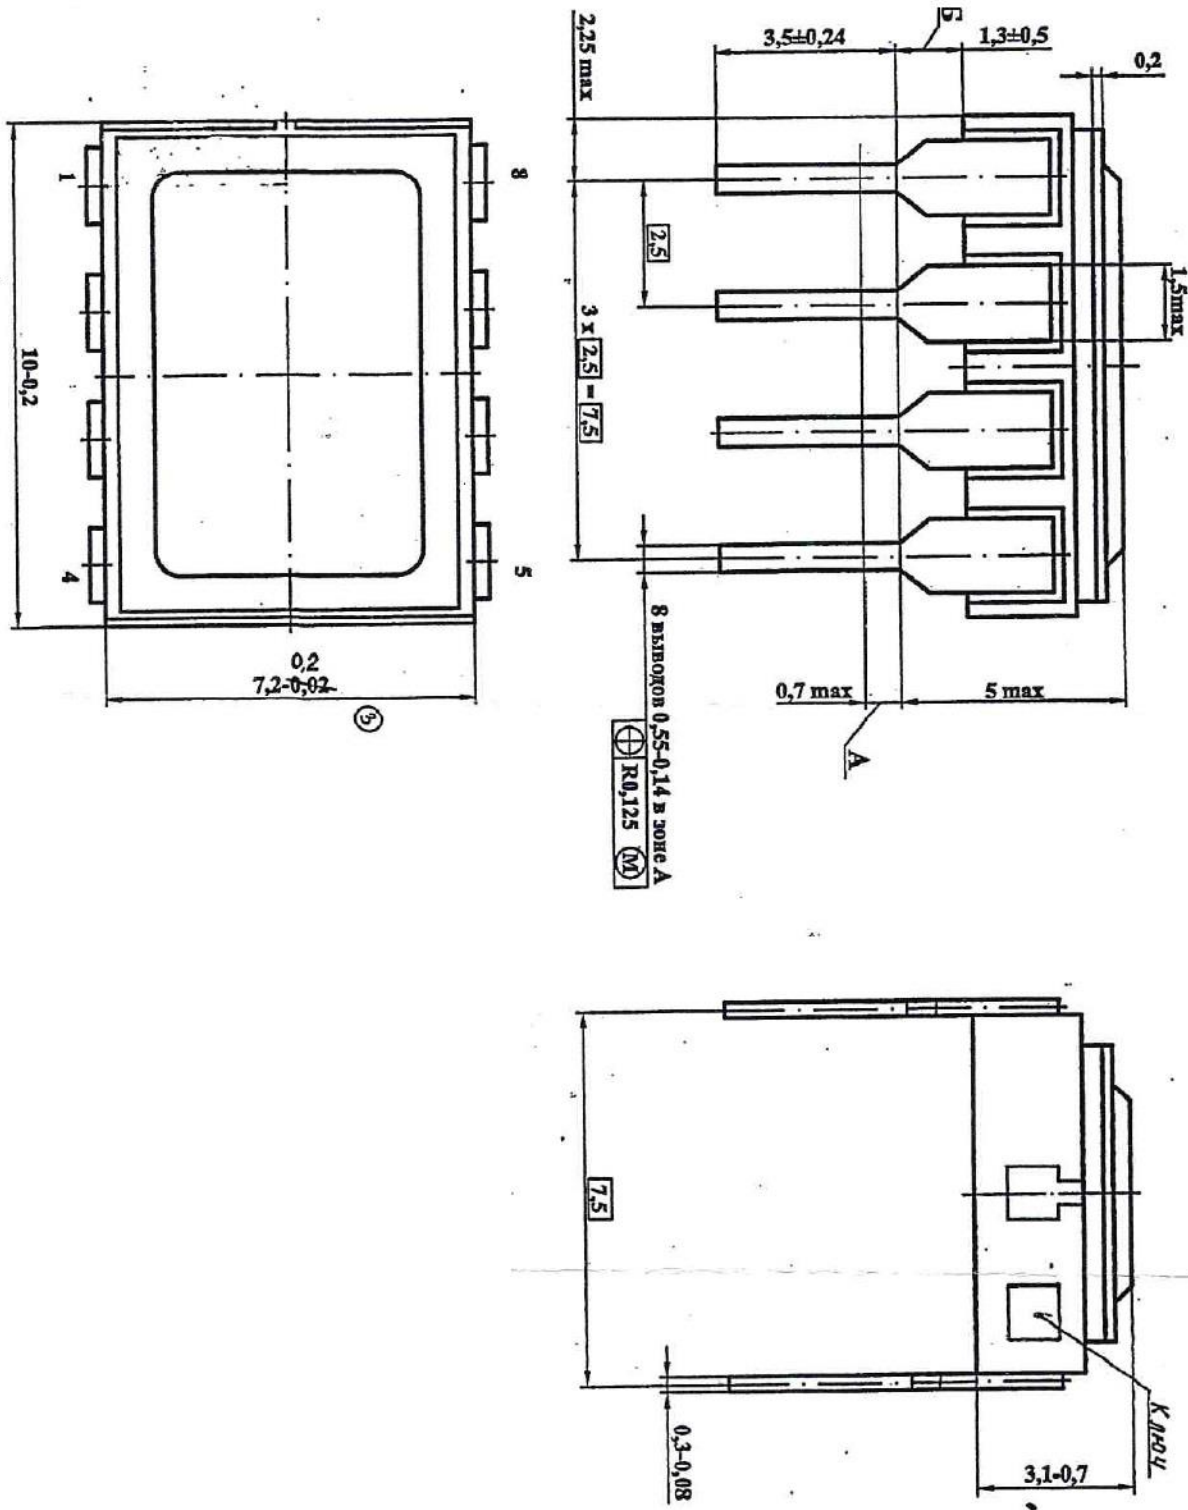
Габаритный чертеж корпуса 2101.8-7
